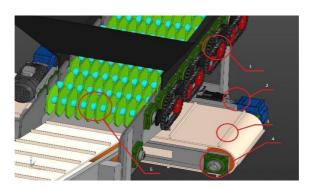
Элементы агрегата Сепаратор опилок: 1 — Звезда 2ПР; 2 — мотор-редуктор; 3 —лента транспортерная; 4 —букса подшипниковая; 5 —вал с металлическими дисками
